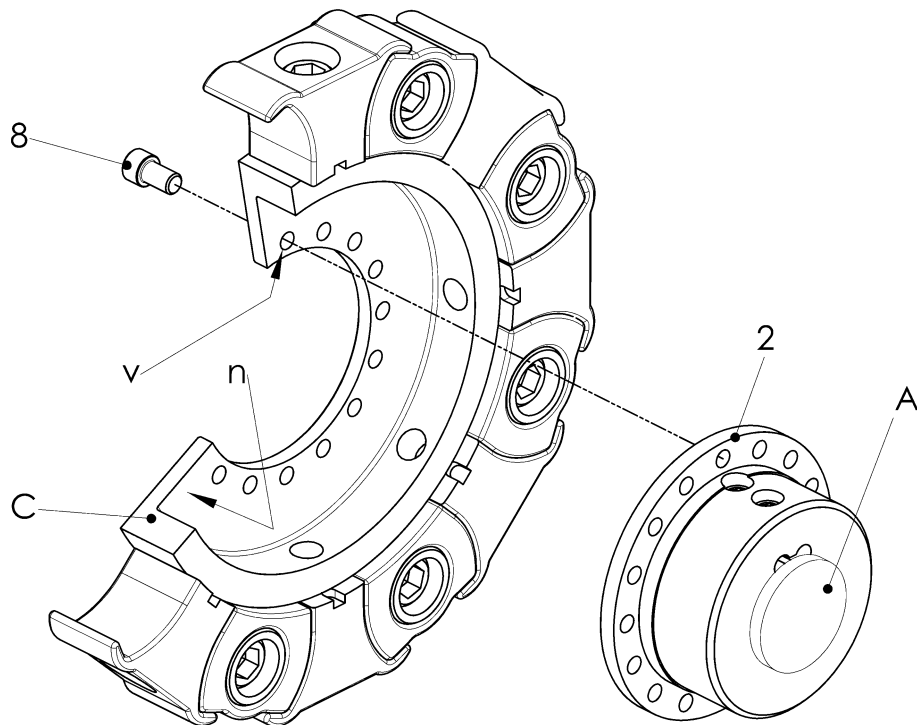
Vormontierte Baugruppe (C) mit Bohrungen (v) an Nabe (2) montieren
